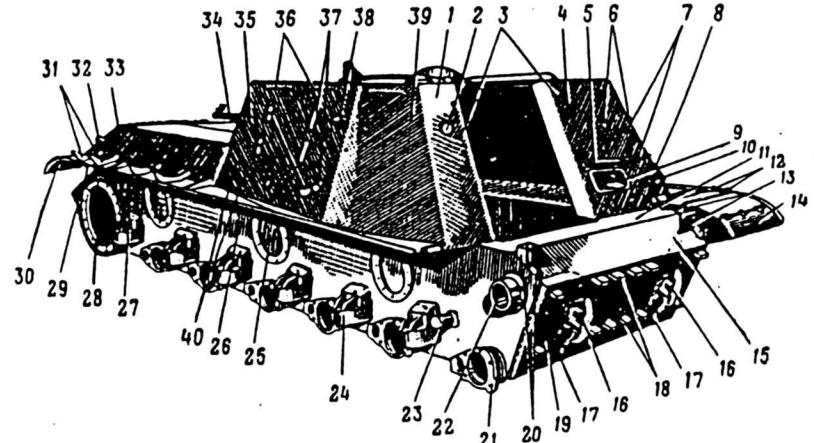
Общий вид корпуса (носовая часть и правый борт):
